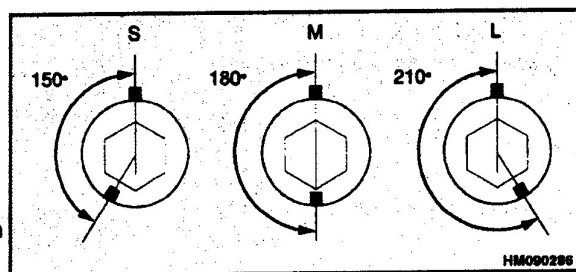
Подтяжка болтов крышки цилиндра, двигателя типа YG и AR
